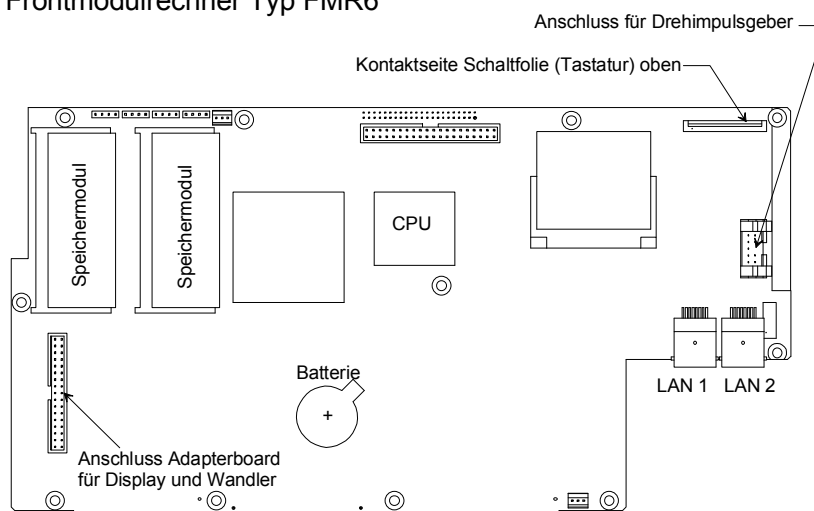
Lage der Steckkontakte auf dem Frontmodulrechner
